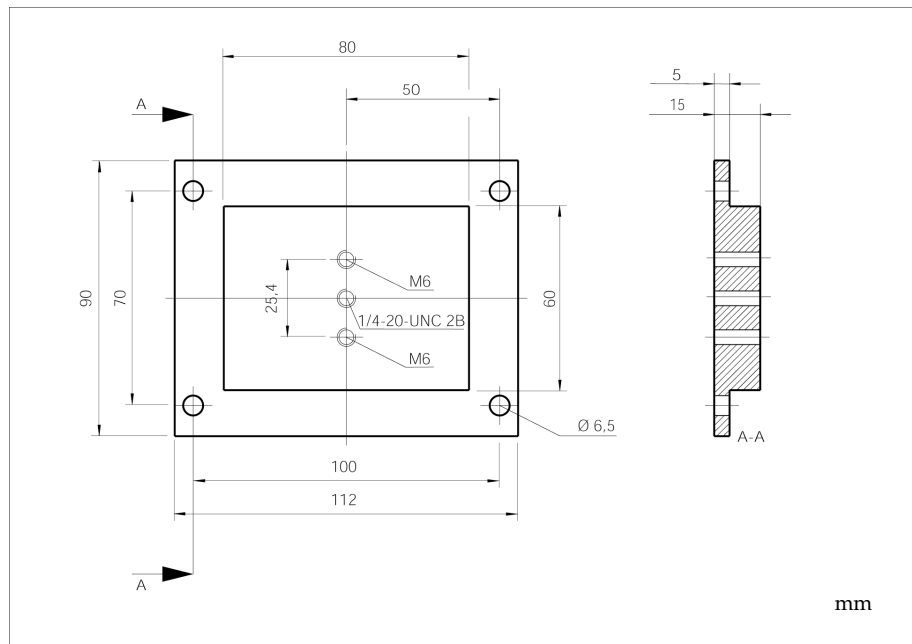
Montageplatte für Stativ mit 1/4" Gewinde
